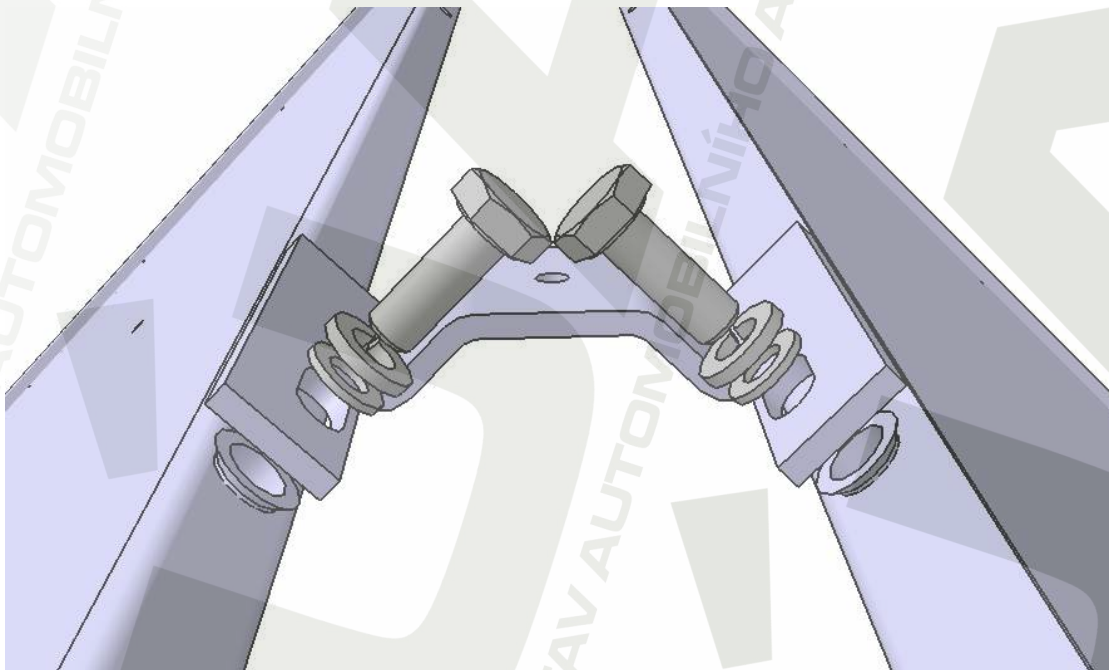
Detail spojení parapetu s rámem společně s profilem tvaru omega
